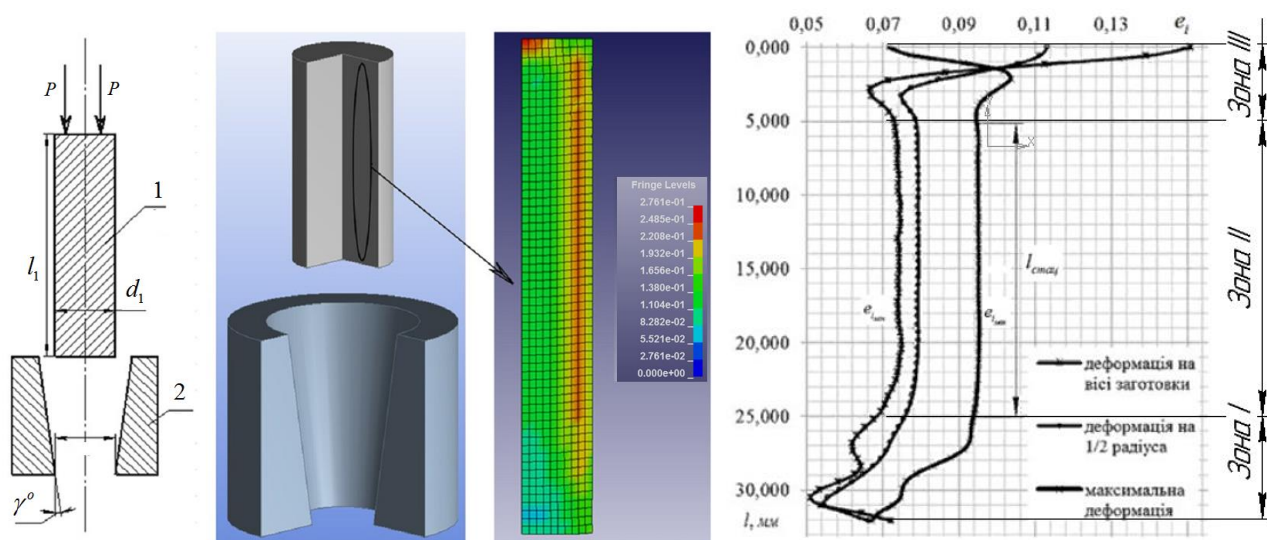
Редукування заготовки (1 – заготовка, 2 – матриця)
